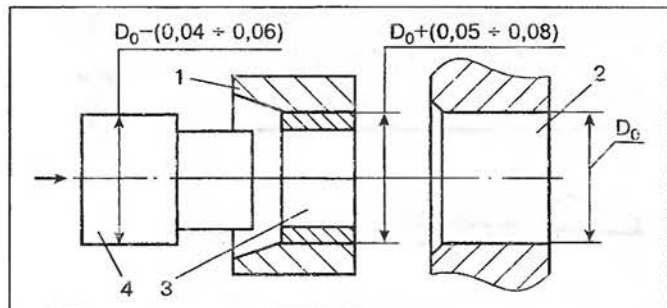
Схема запрессовки втулки, выполненной из двух половин: 1 — оправка; 2 — опора; 3 — втулка; 4 — толкатель
